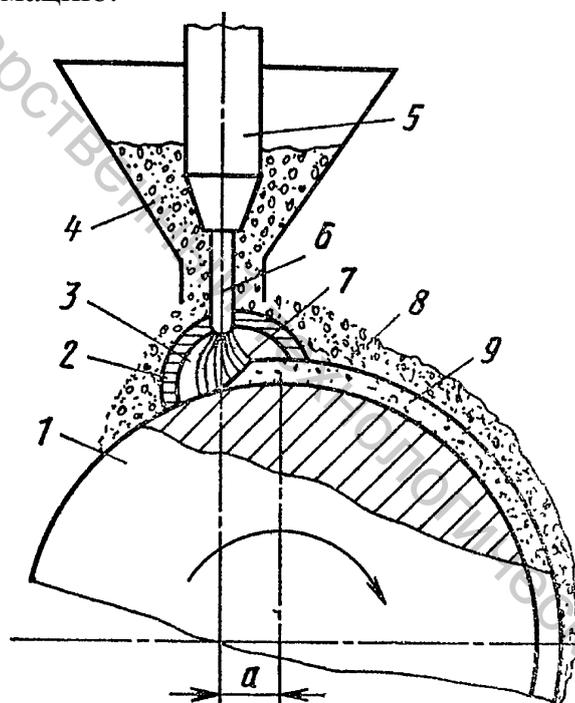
Схема автоматической наплавки: 1 – наплавляемая деталь; 2 – оболочка жидкого флюса; 3 – эластичная оболочка; 4 – бункер с флюсом; 5 – мундштук; 6 – электрод; 7 – электрическая дуга; 8 – шлаковая корка; 9 – наплавленный металл; а – смещение с зенита детали
